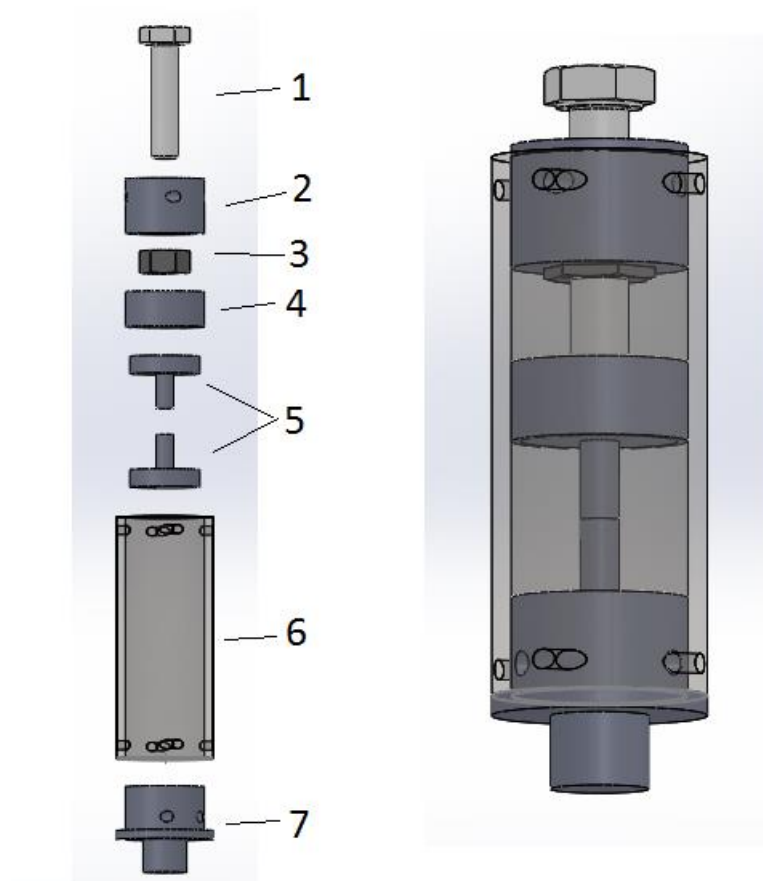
Explosionado y conjunto soporte: 1) Tornillo; 2) Cubierta tuerca; 3) Tuerca; 4) Cubierta superior; 5) Piezas metálicas; 6) Tubo de plástico; 7) Base.
